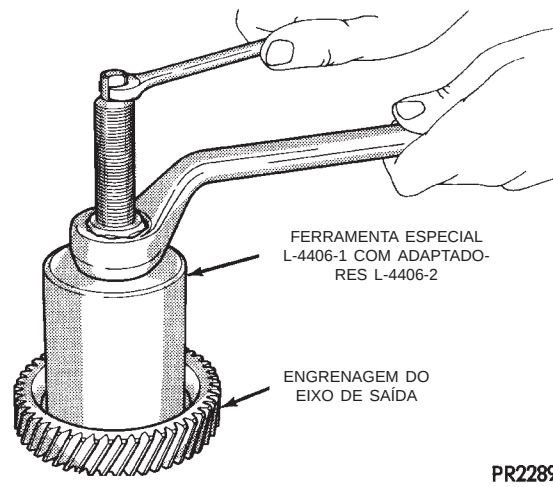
Remoção do Cone de Rolamento da Engrenagem do Eixo de Saída
